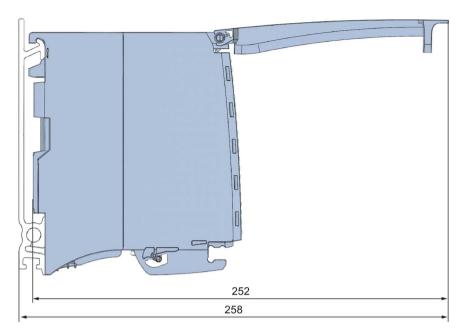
Maßbild des Moduls DI 32x24VDC HF in Seitenansicht mit geöffneter Frontklappe
